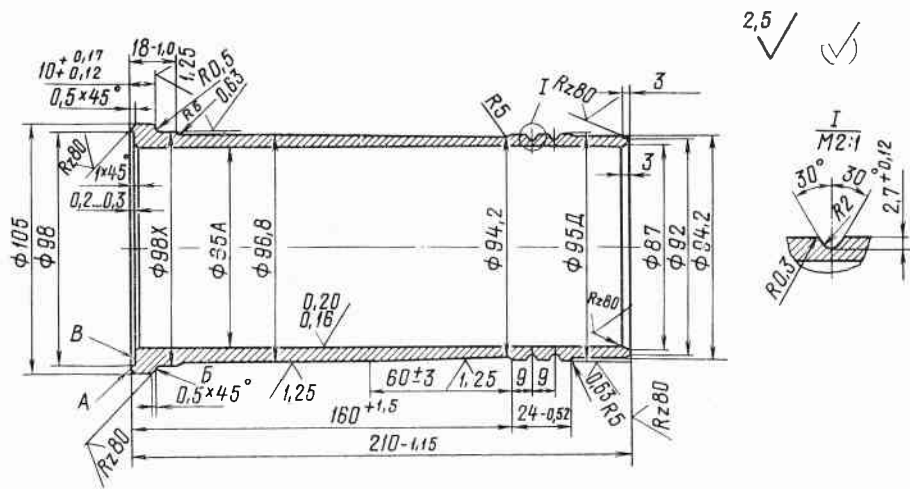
Втулка цилиндра — 5Д2-13.00.02 Fig. 68. Cylinder liner, 5Д2-13.00.02
